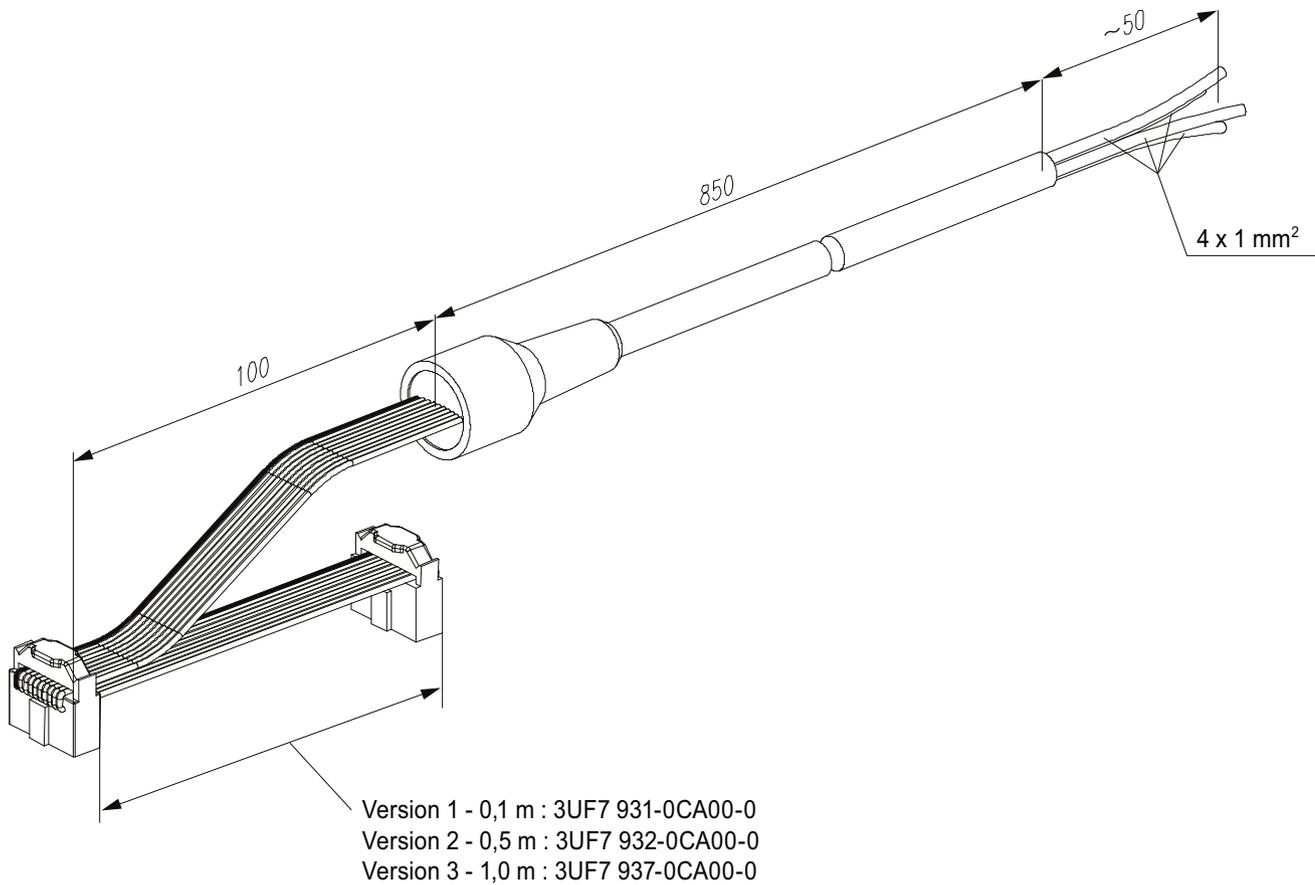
Plan d'encombrement du câble de liaison en Y
